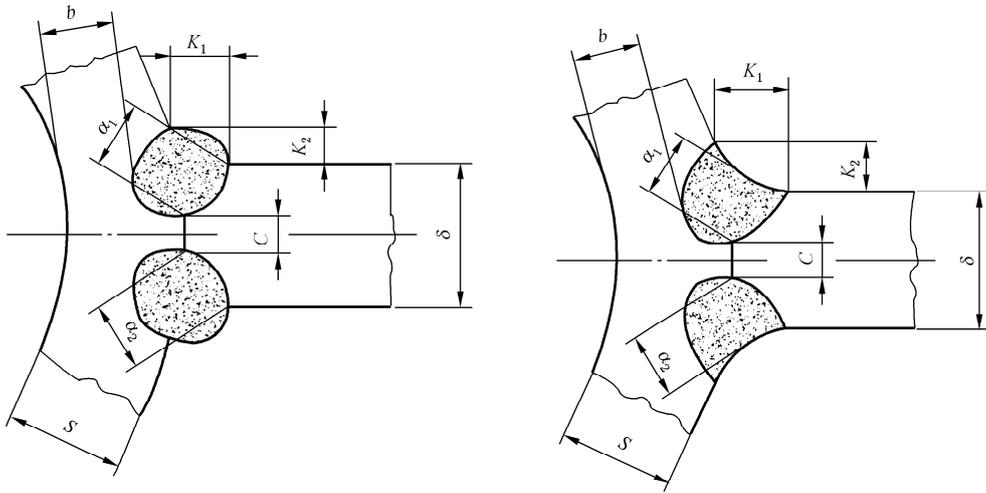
埋弧焊钢管与扁钢的焊接熔深要求
